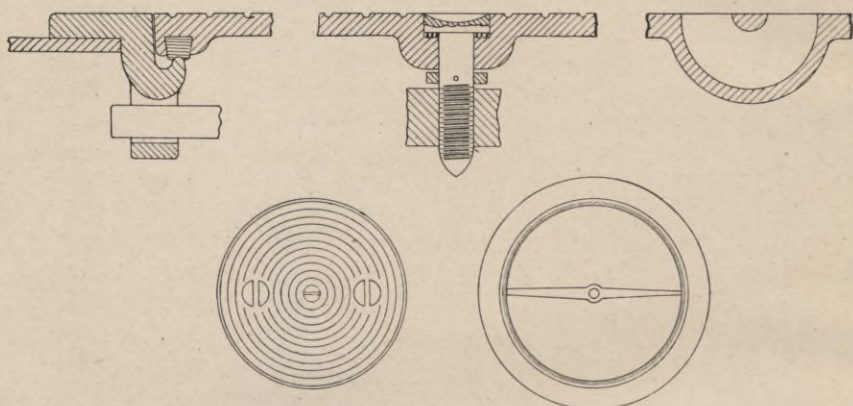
Deckel mit Knebel und Gewindebolzen.
